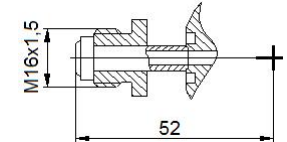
Штуцер (входной) для торцевого уплотнения Ni шайбой с втулкой с метрической резьбой M16x1,5
